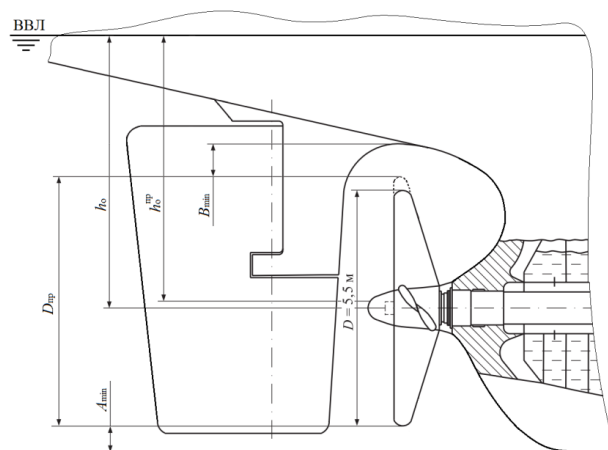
Кормова кінцівка танкеру типу «Дмитрий Медведев»
